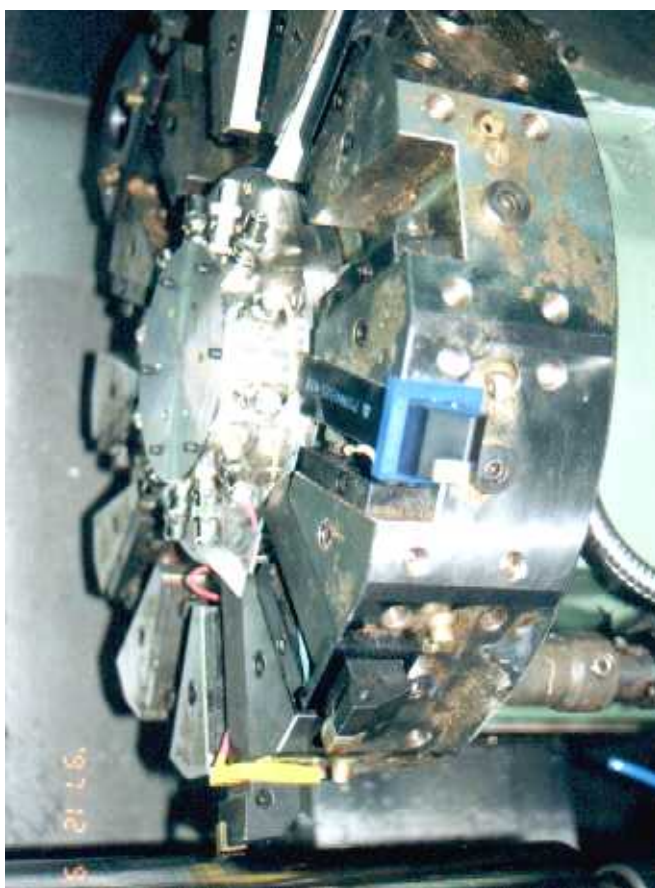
Приклад виконання комутатора для токарного верстата
